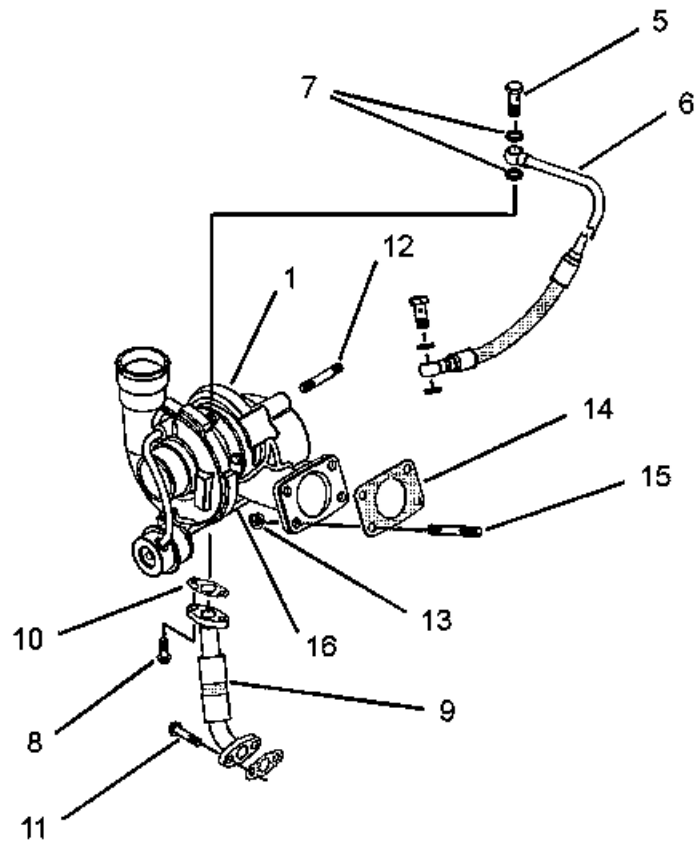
Turbocompresor del Sistema de admisión de motor Perkins
